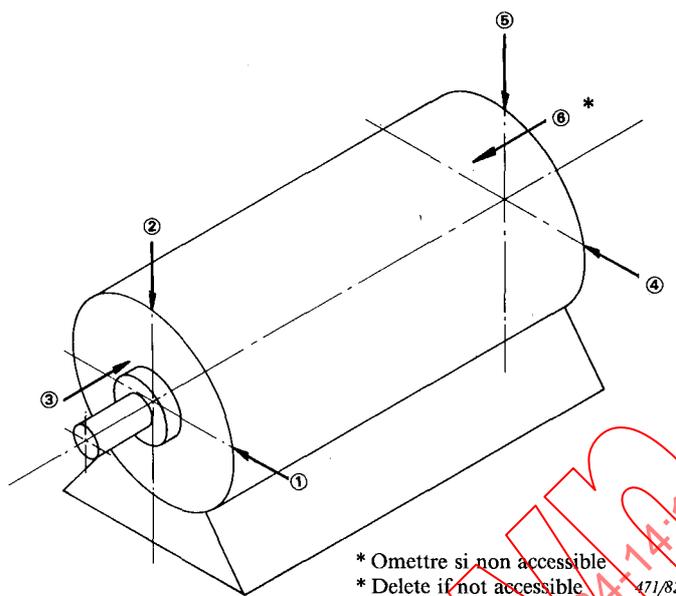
Emplacement des points de mesure pour des machines de hauteur d'axe de 56 mm à 400 mm inclus.
